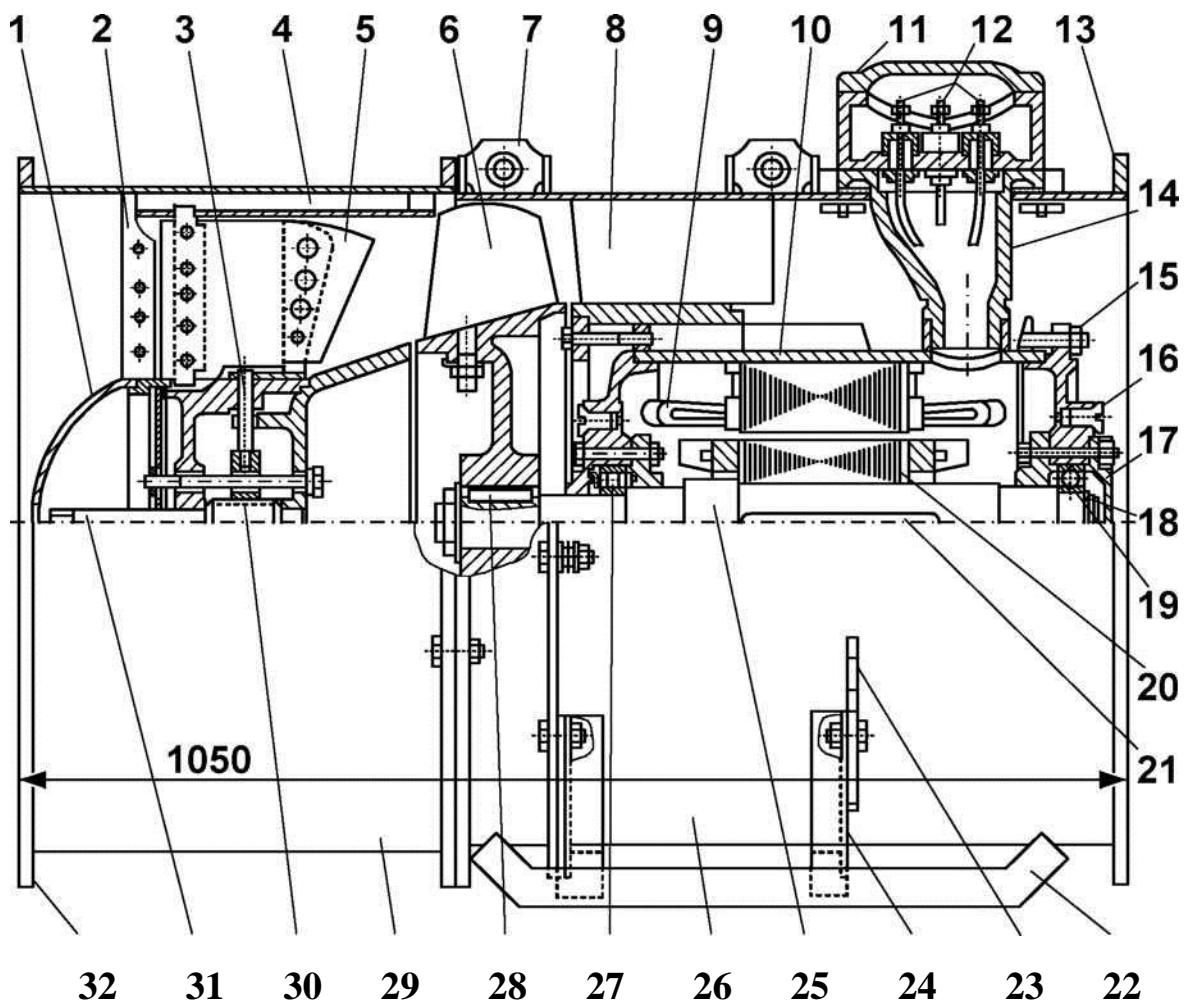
Вентилятор ВМ-6М: 1 - передний обтекатель (кок); 2 - ограждающая решетка; 3, 30 и 31 - привод лопаток направляющего аппарата; 4 - противосрывное устройство; 5 - лопатки направляющего аппарата; 6 - рабочее колесо; 7 - рым для подвески вентилятора; 8 - лопатки спрямляющего аппарата (опоры для крепления двигателя к корпусу вентилятора); 9 - обмотки возбуждения статора; 10 - оболочка электродвигателя; 11 и 14 - крышка и горловина кабельного ввода; 12 - шпильки двигателя; 13 и 32 - отводящий и подводный фланцы; 15 - фиксатор; 16 - заглушка; 17 - глухой фланец; 18 - стопорное кольцо; 19 и 27 - задний и передний подшипники; 20 - ротор; 21 и 28 - шпонки ротора и рабочего колеса; 22 - салазки; 23 и 24 - кронштейн и стойка; 26 и 29 - задняя и передняя части корпуса
